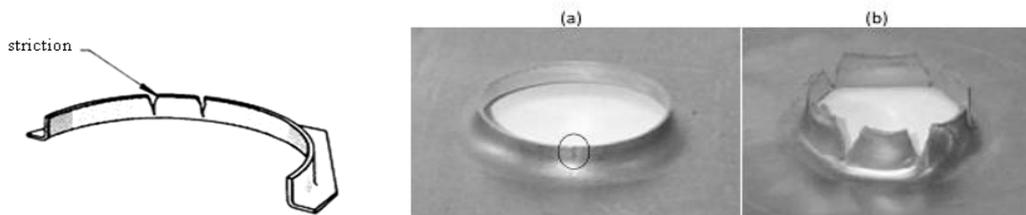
Exemples de défauts : (a) strictions (b) déchirures axiales
